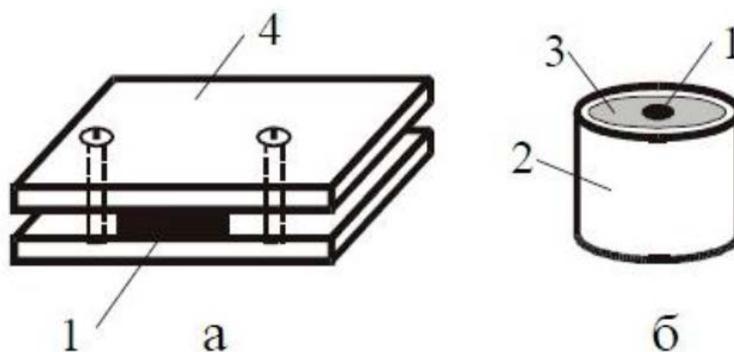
Приспособления для приготовления микрошлифов: а) шлиф, зажатый в струбцине; б) шлиф, залитый эпоксидной смолой [18]
